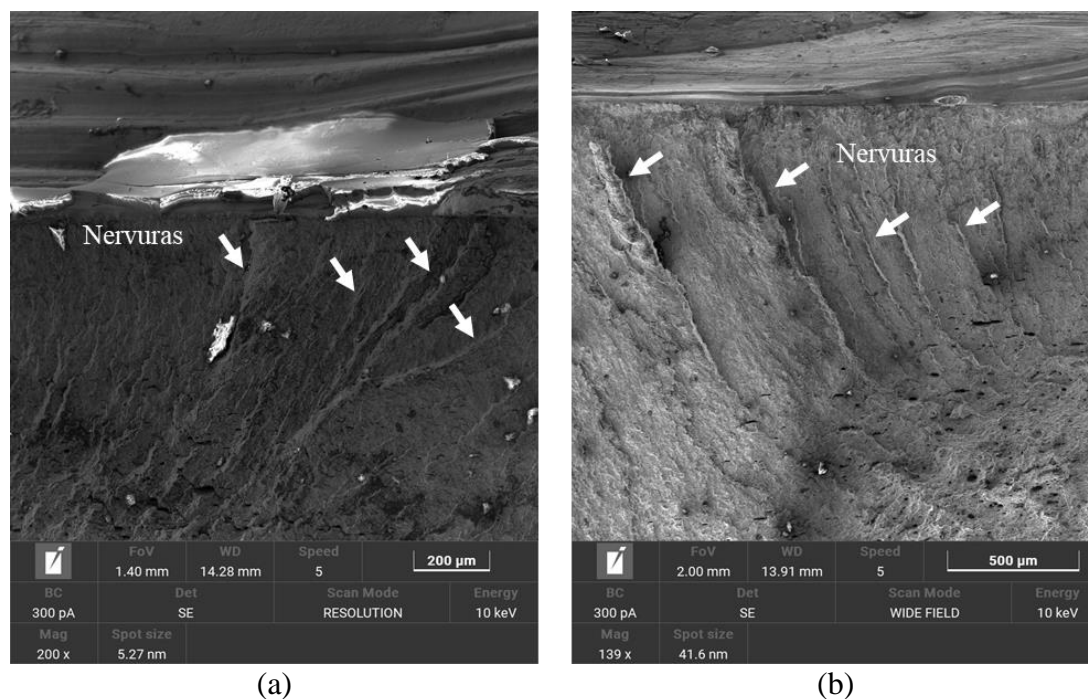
Superfície de fratura do metal soldado com cordão e ponto de solda, ampliada em 50x e ensaiado na tensão máxima de 350 MPa
